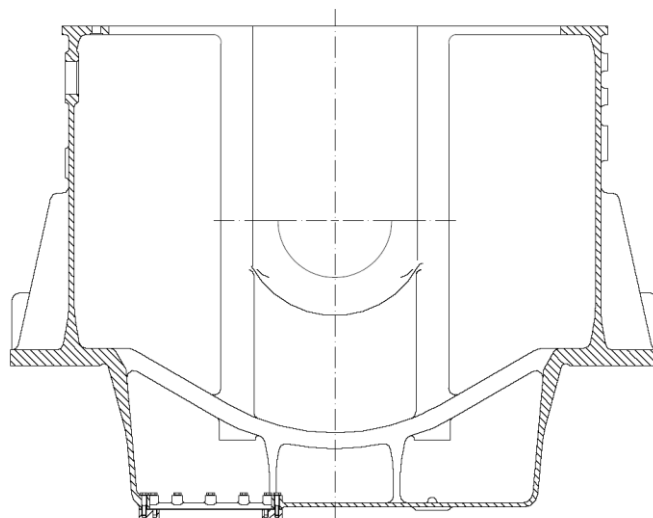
Фундаментна рама головного двигуна 8ДКРН 26/98
